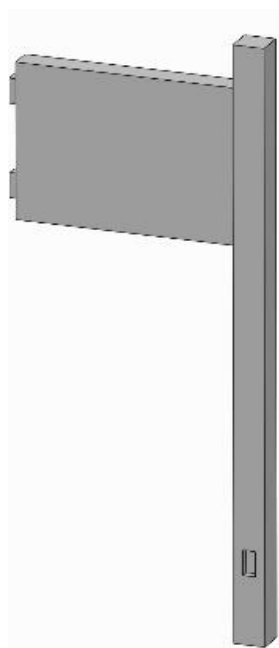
Unión plancha + horizontal || Fuente: Elaboración propia
